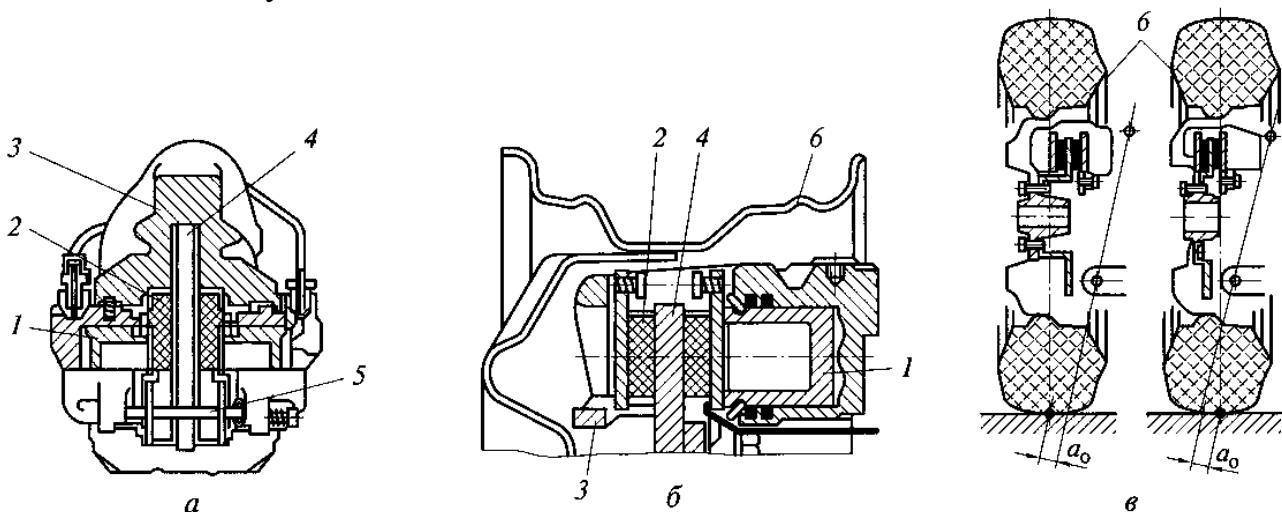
Схеми дискових гальмівних механізмів з нерухомою (*a*), рухомою (*б*) скобами і установка скоб (*в*):
